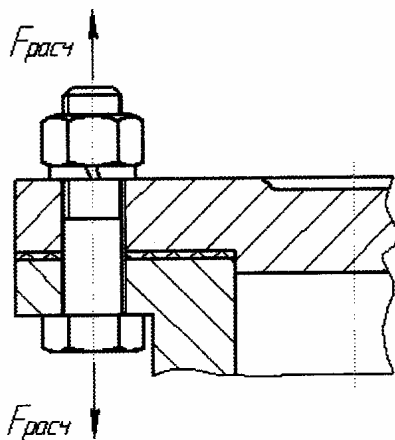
Схема для расчета болтового напряженного резьбового соединения без внешней нагрузки
